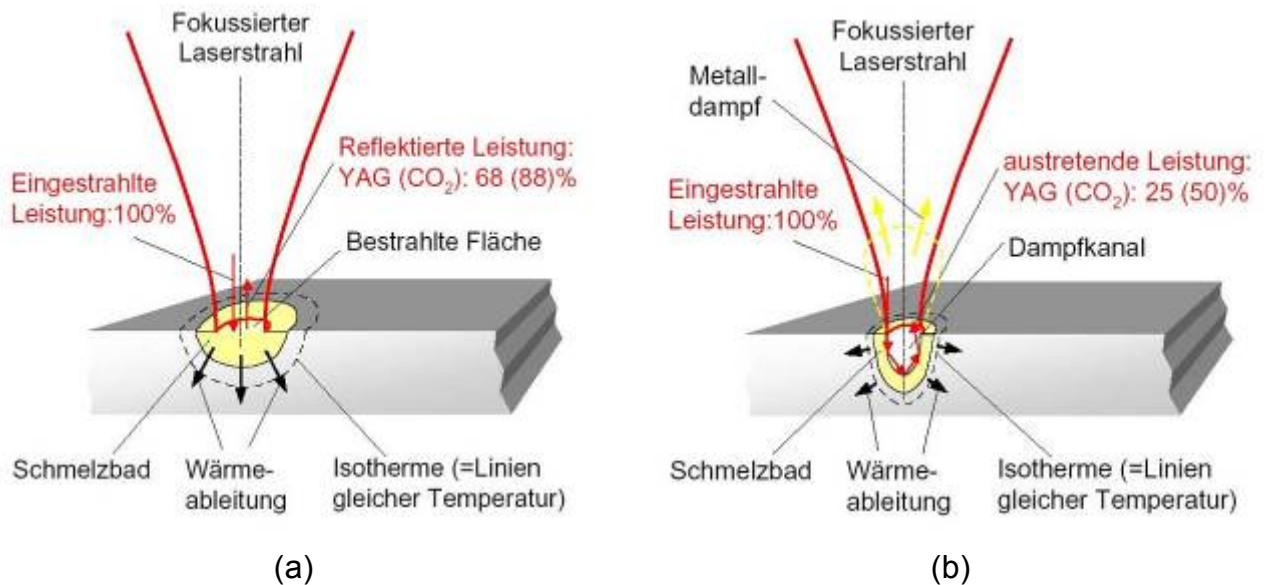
Prinzip des Laserstrahlschweißens; a) Wärmeleitungsschweißen; b) Tiefschweißen [46]
